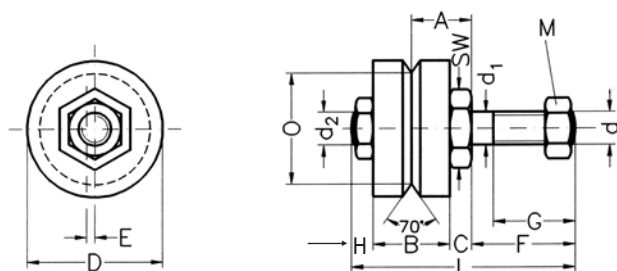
70° RL-Rolle mit langem Bolzen | Fig.1: 70° RL-Roller with long bolt
